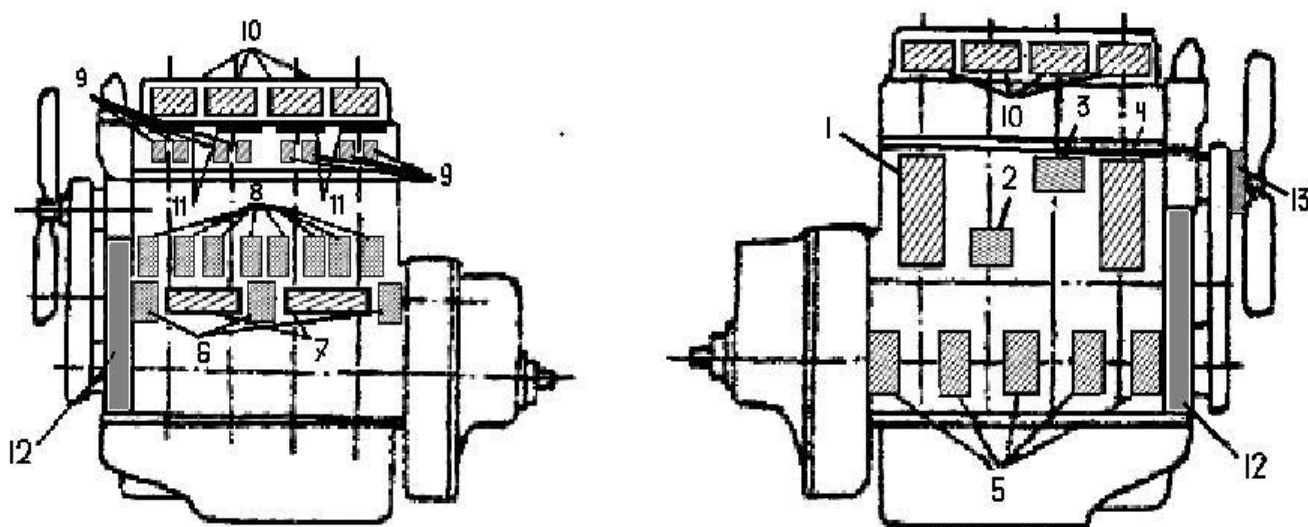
Зоны ослушивания двигателей: 1 – цилиндро-поршневой группы, 2 – поршневых колец, 3 – поршневых пальцев и втулок шатуна, 4 – шатунных подшипников, 5 и 6 – подшипников распредвала, 7 и 8 – толкателей, 9 – втулок клапанов, 10 – стержней клапанов, 11 – клапанов и днищ поршней, 12 – распределительных шестерен
